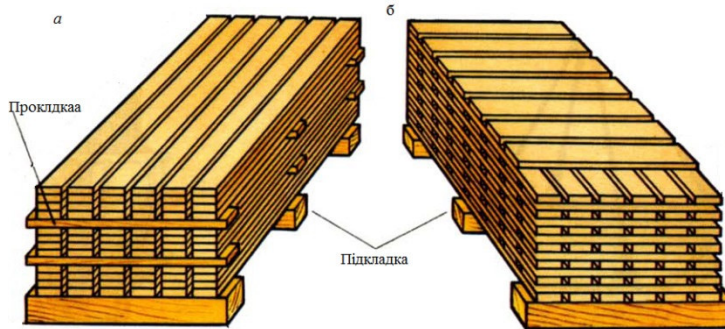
Складування пиломатеріалів: а – укладка рядами; б – укладка у клітку
